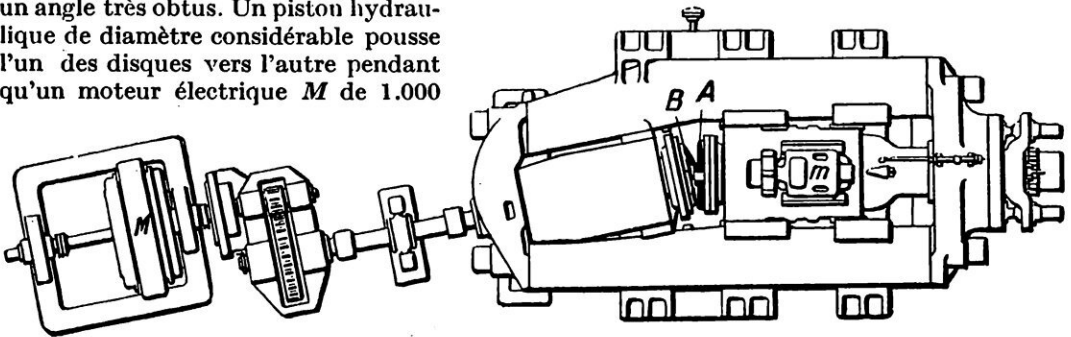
PLAN D'ENSEMBLE DE LA MACHINE SLICK POUR LAMINER LES ROUES DE WAGONS
